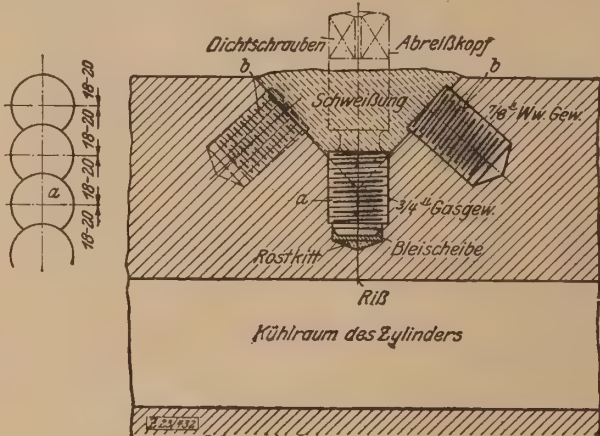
Ausgeführte Zylinderschweißung.
